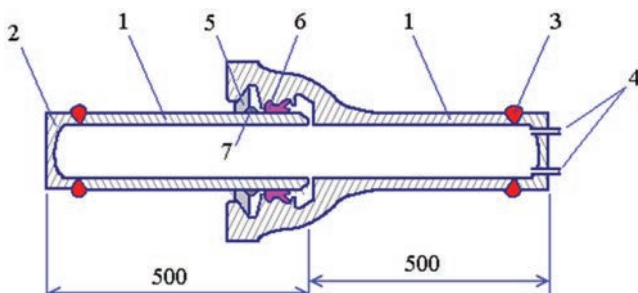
Образец для гидроиспытаний соединения «RJ»
